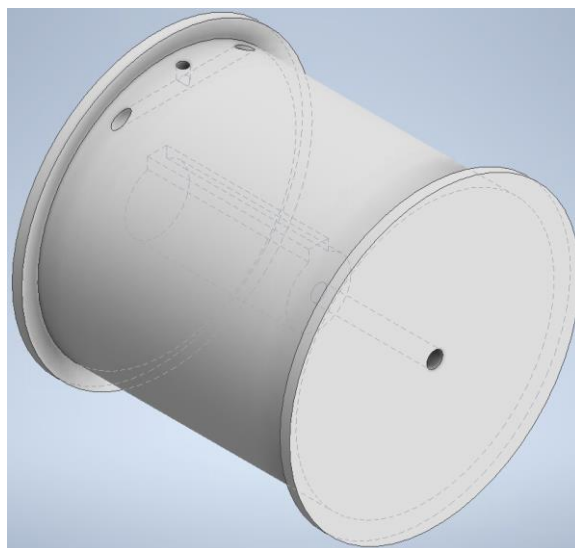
3D-модель сборки приводного модуля стенда
